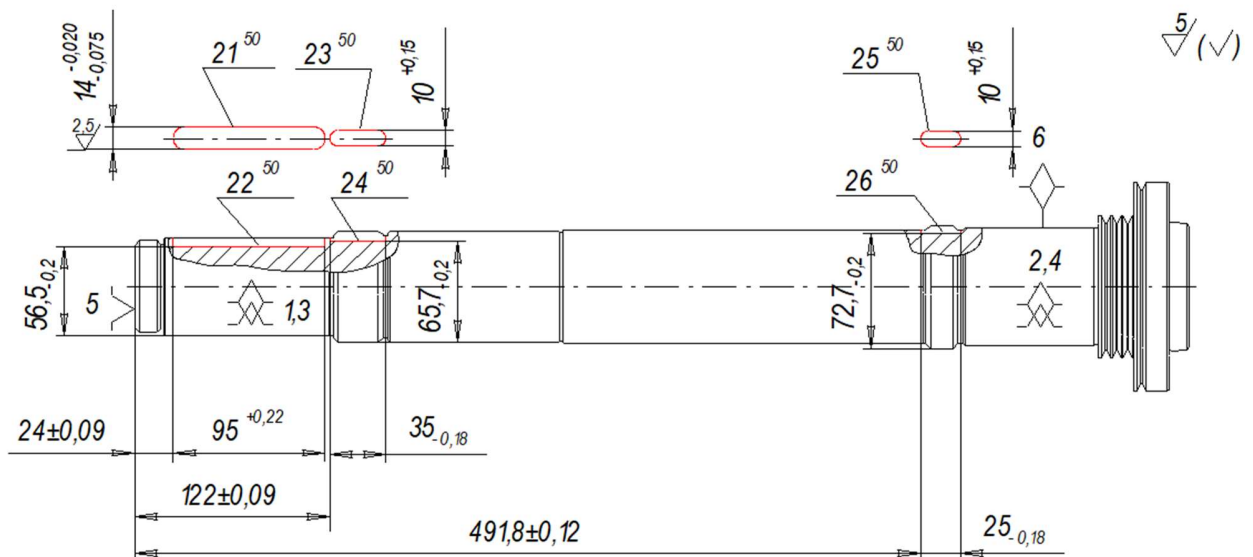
Схема базування для фрезерування шпонкових пазів
